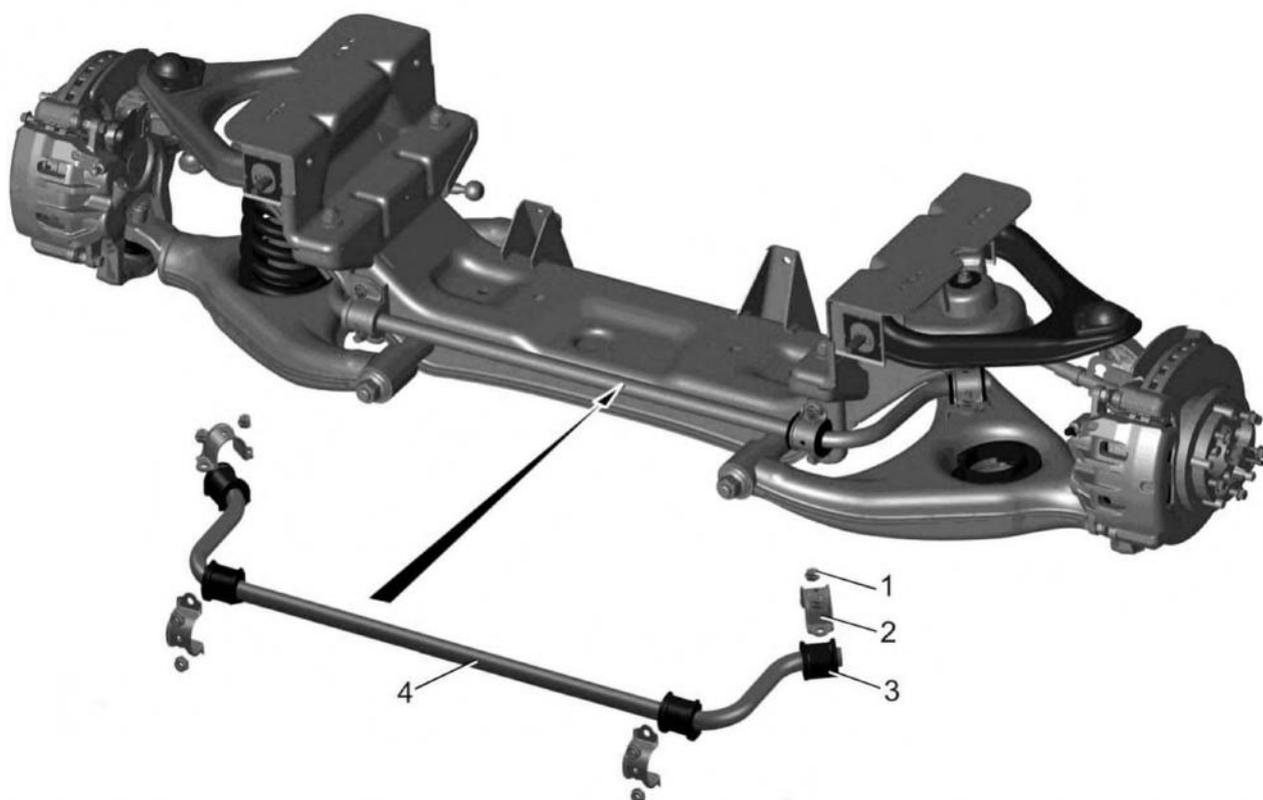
Установка стабилизатора поперечной устойчивости: 1 – гайка; 2 – скоба подушки; 3 – подушка; 4 – штанга стабилизатора
